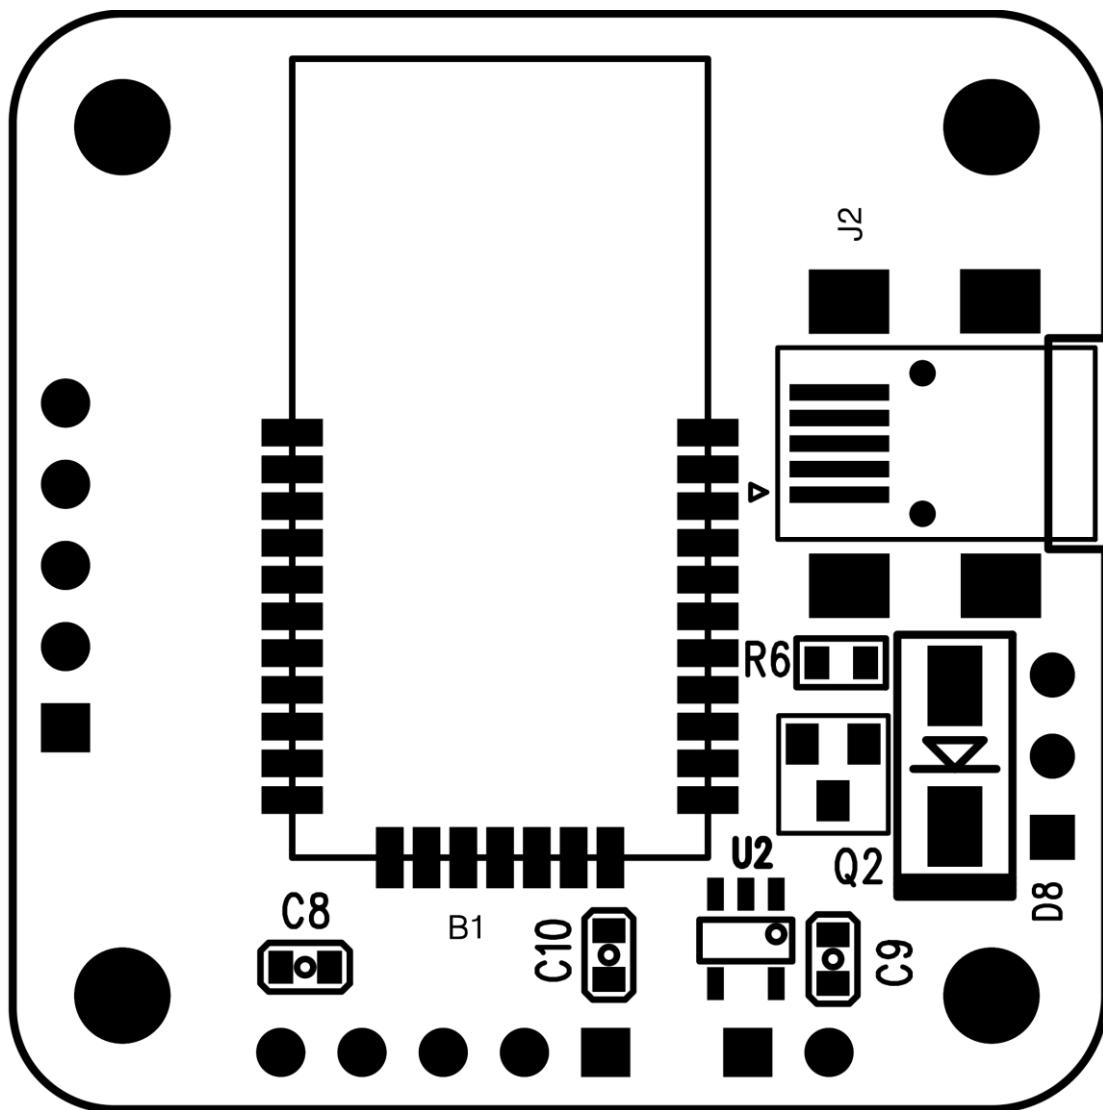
AHRS 模組通信端反面 PCB 佈局
